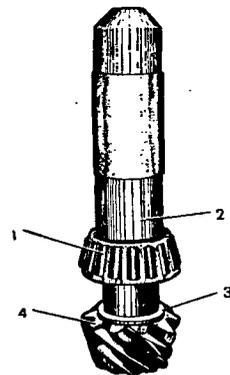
Установка внутреннего кольца заднего подшипника на ведущую шестерню: 1 - внутреннее кольцо заднего роликоподшипника; 2 - оправка А.70152; 3 - регулировочное кольцо; 4 - ведущая шестерня
